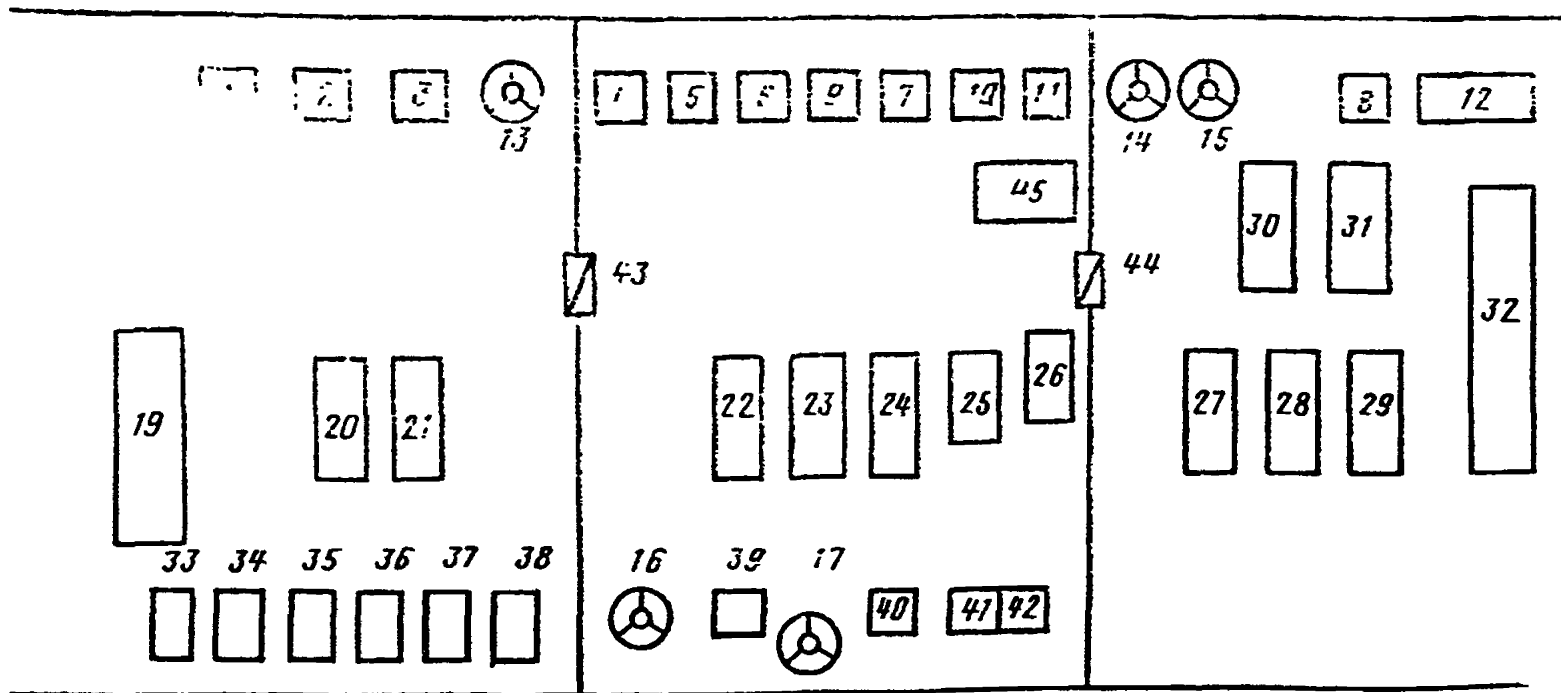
Типовая схема организации рабочего места сборки двигателя:
